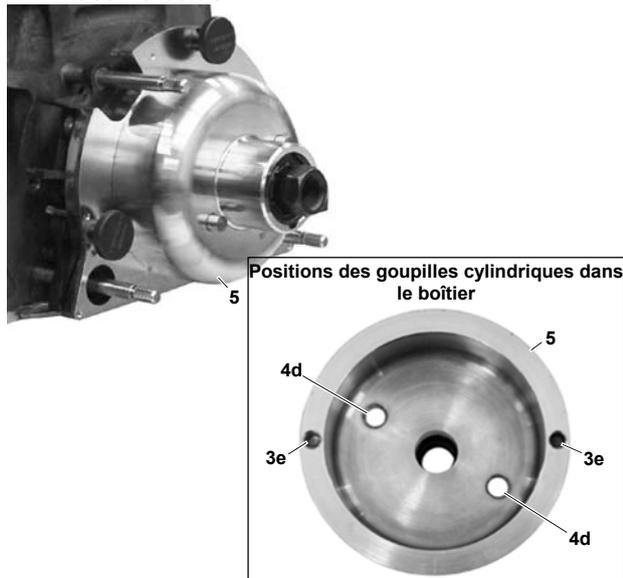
Visser le boîtier avec écrou sur la tige filetée.
